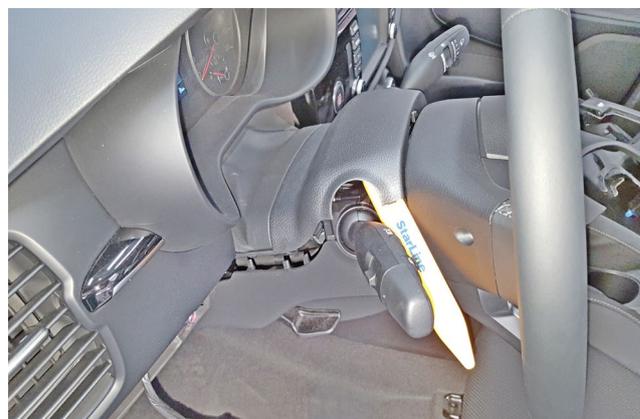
Снять верхнюю часть кожуха рулевого вала
